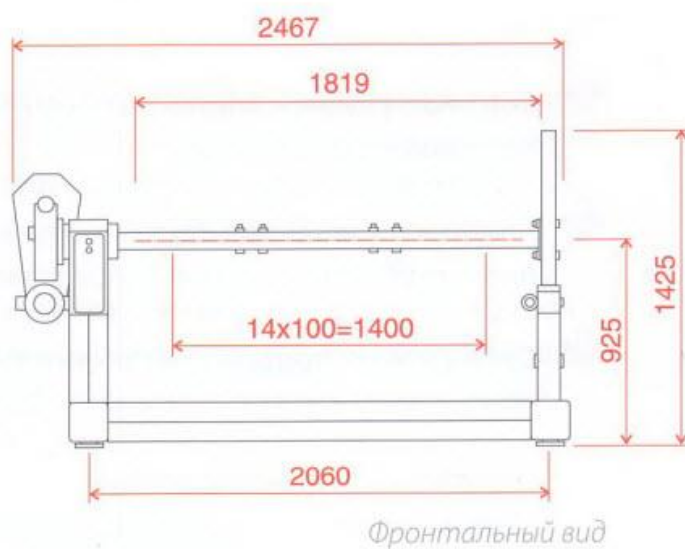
Стенд Р-776Е (габаритные размеры)
